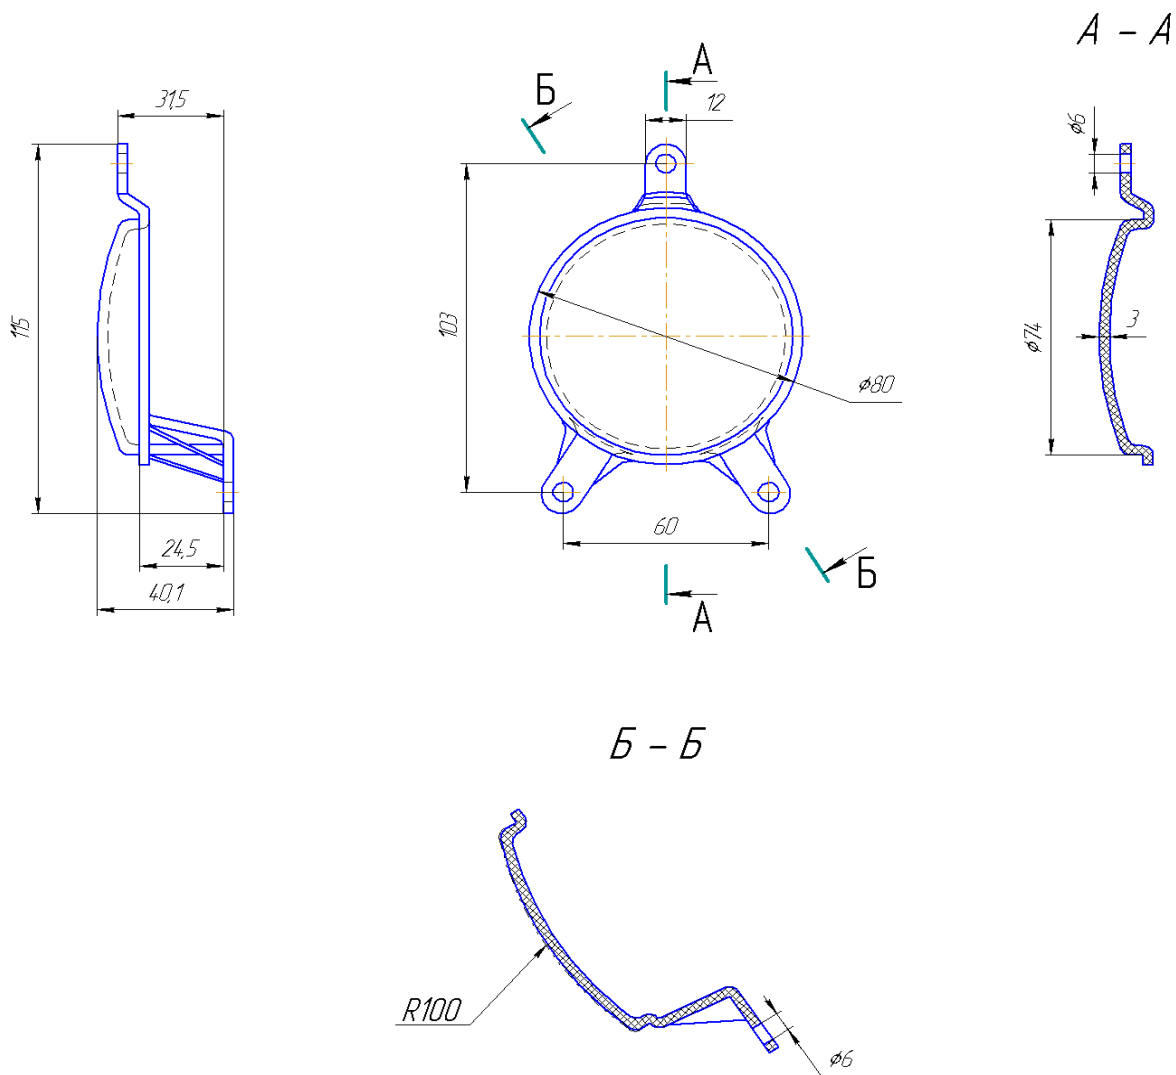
Чертеж базовой детали «Заглушка переднего бампера»
